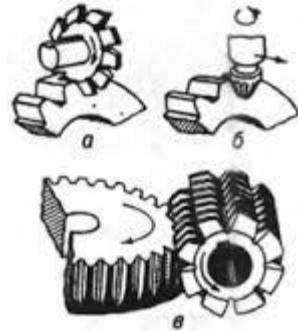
Схема нарезания зубчатых колес методом обкатки:
